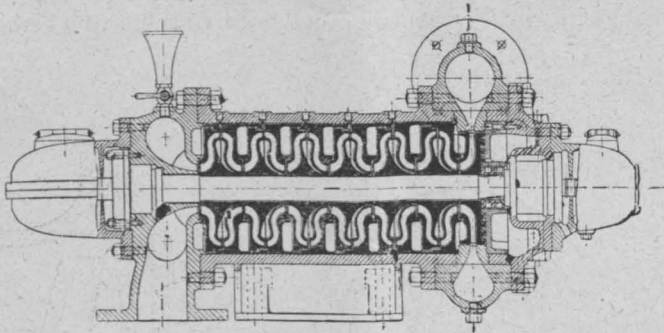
Längenschnitt einer Kugel-Gelpcke-Pumpe.
